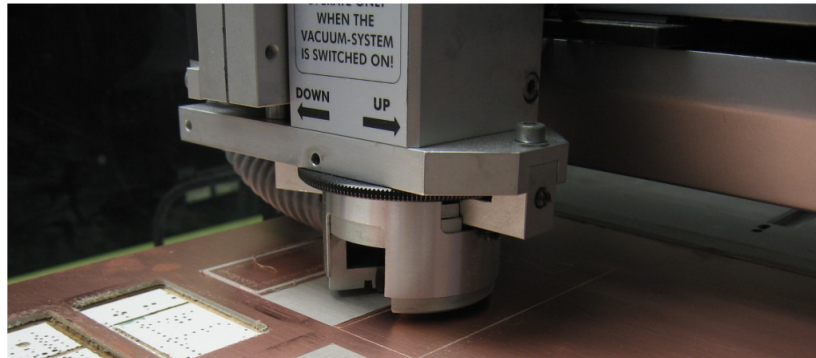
Máquina Fresadora realizando el circuito impreso.
